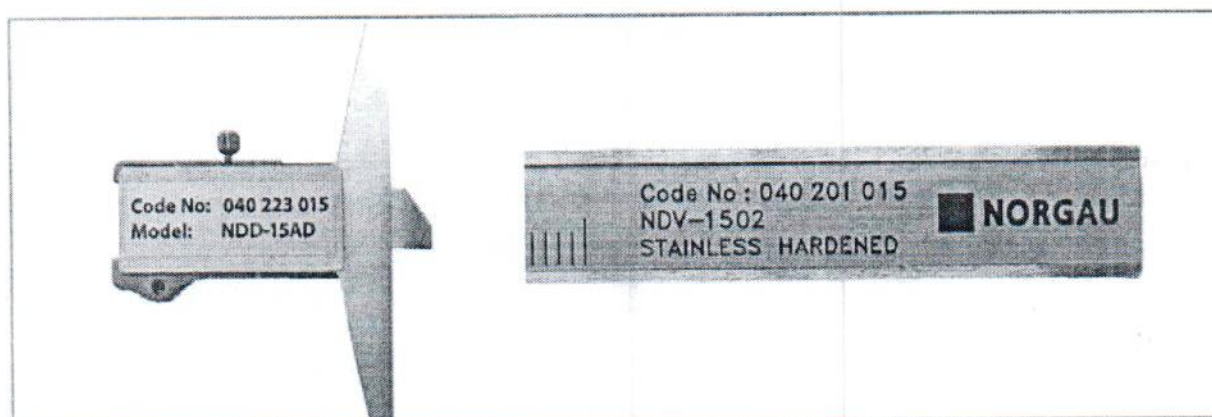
Общий вид маркировки модификации штангенглубиномеров
